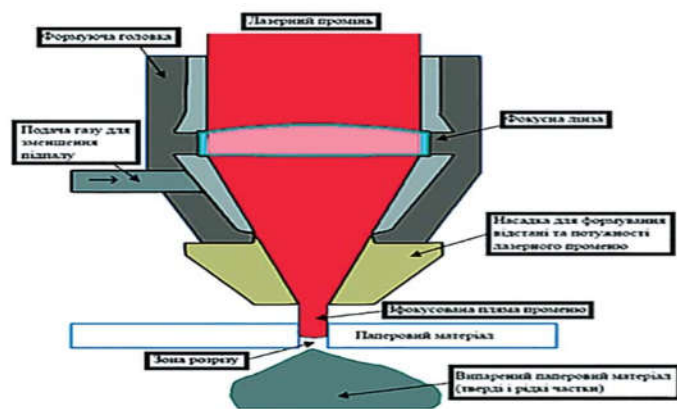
Принципова схема візуалізації процесу різання паперових заготовок упаковки
